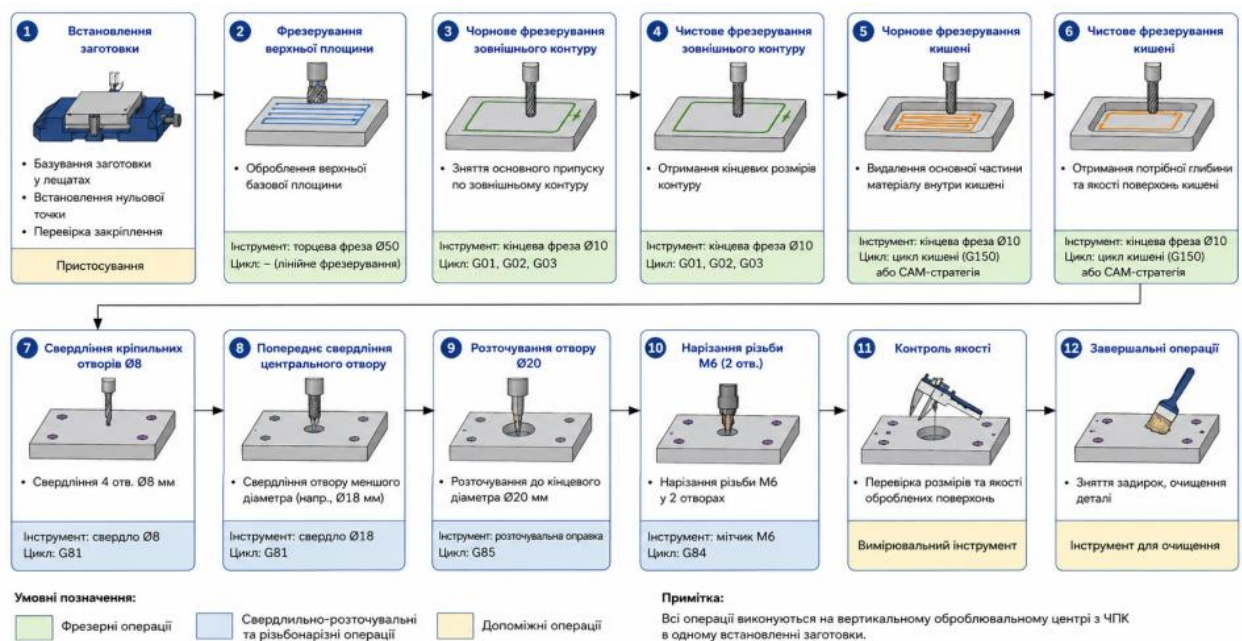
Загальна схема технологічного маршруту оброблення деталі на верстаті з ЧПК
